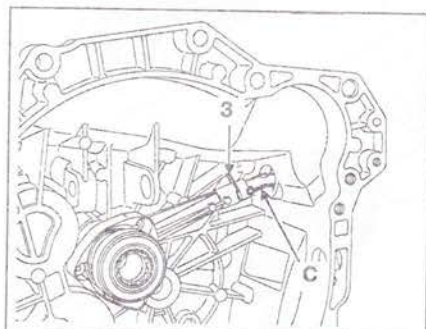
Отсоедините штуцер С рабочего цилиндра привода выключения сцепления, сняв фиксатор 3.
